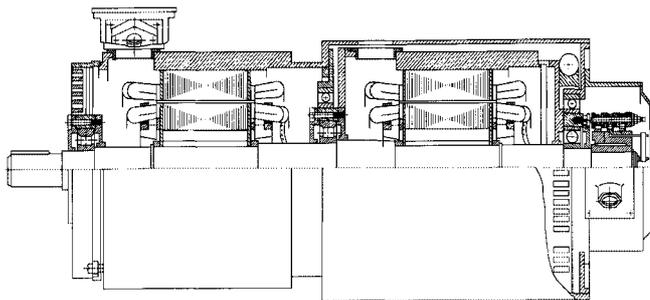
Тяговая асинхронная плавнорегулируемая двухдвигательная установка с поворотным статором одного двигателя
